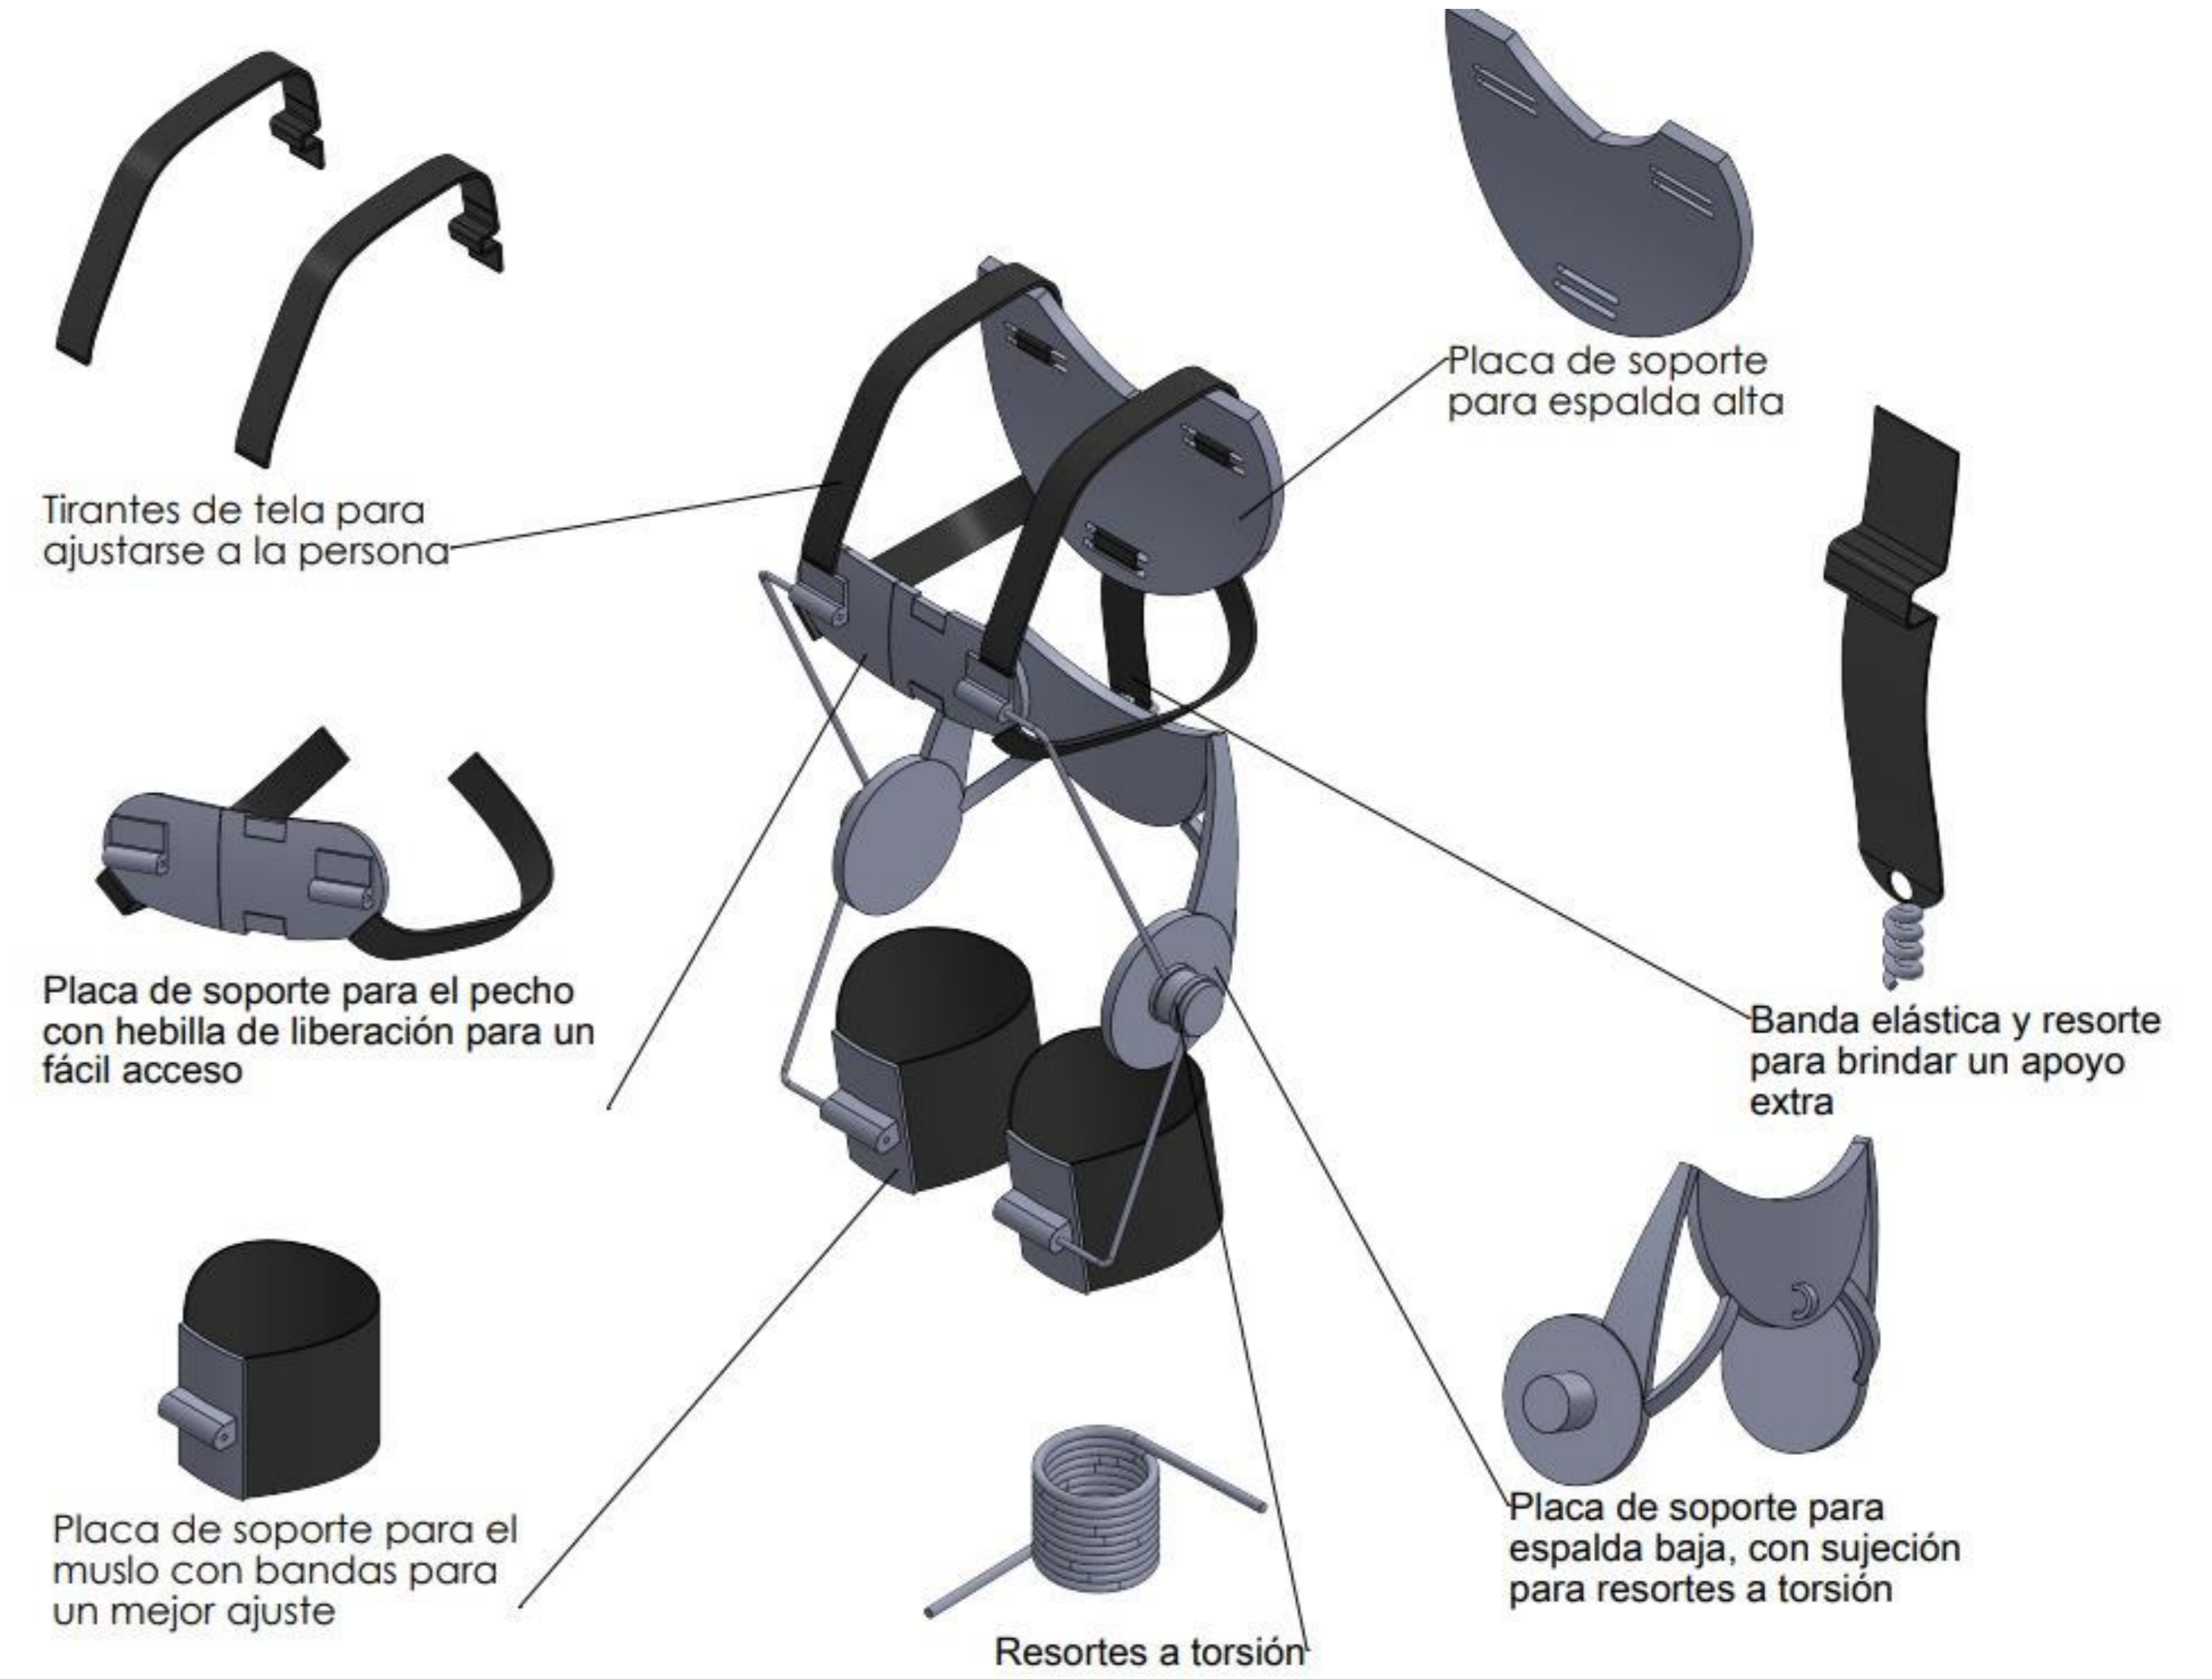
Diseño preliminar, vista isométrica con despiece descriptivo
